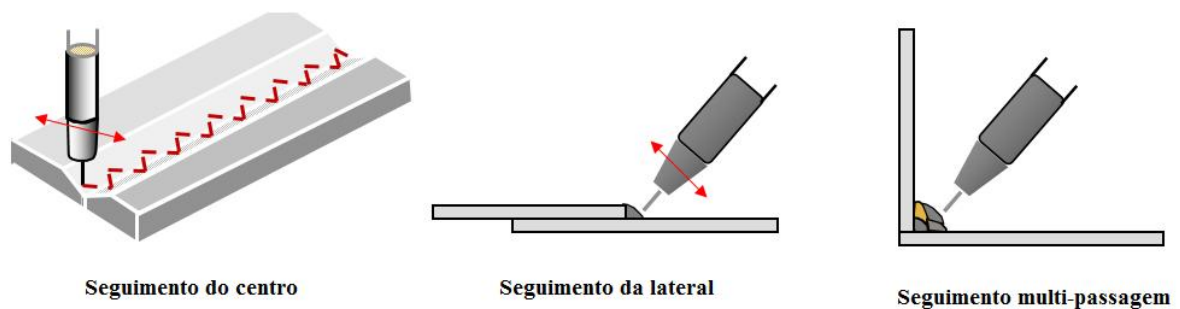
Formatos de um seguimento de junta de soldadura
